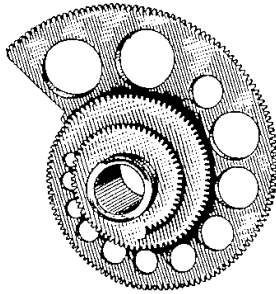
Engranaje para transmisión de movimiento axial y giratorio. [1]
